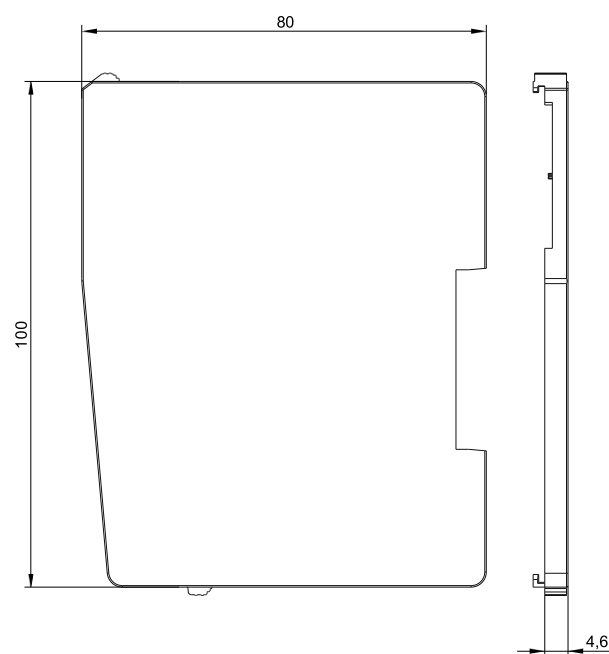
Габаритные и установочные размеры модуля клеммной крышки
